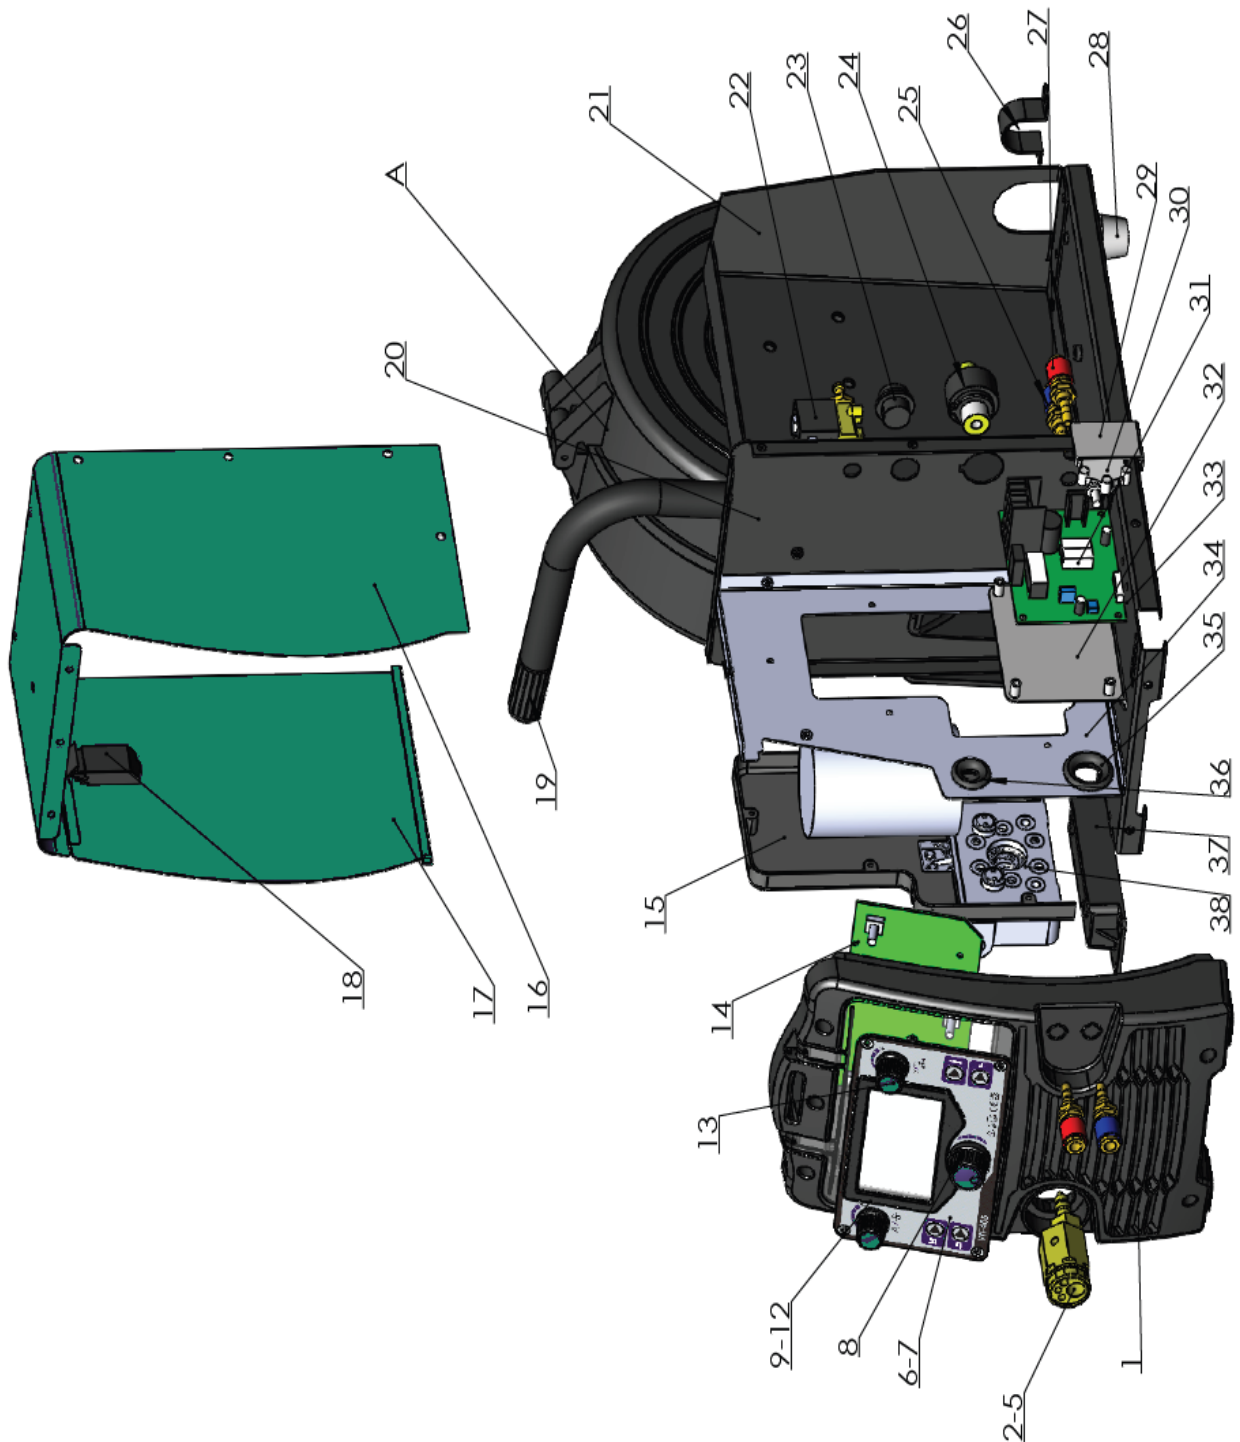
Vista explodida alimentador externo Vulcano Flex MIG 510i.
